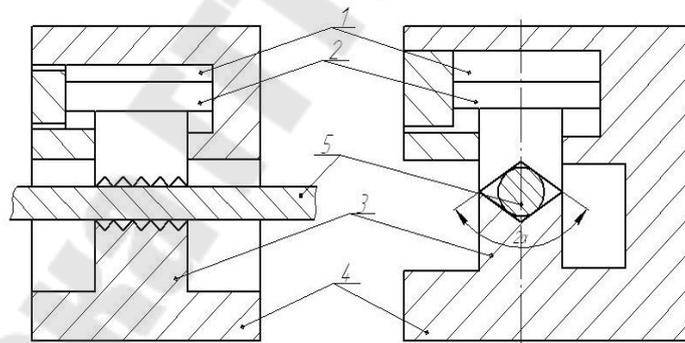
Схемы клещевых захватов: 1 - пневмо- или гидроцилиндр, 2 – подвижная губка клещей, 3 - неподвижная губка клещей, 4 - корпус, 5 - заготовка
